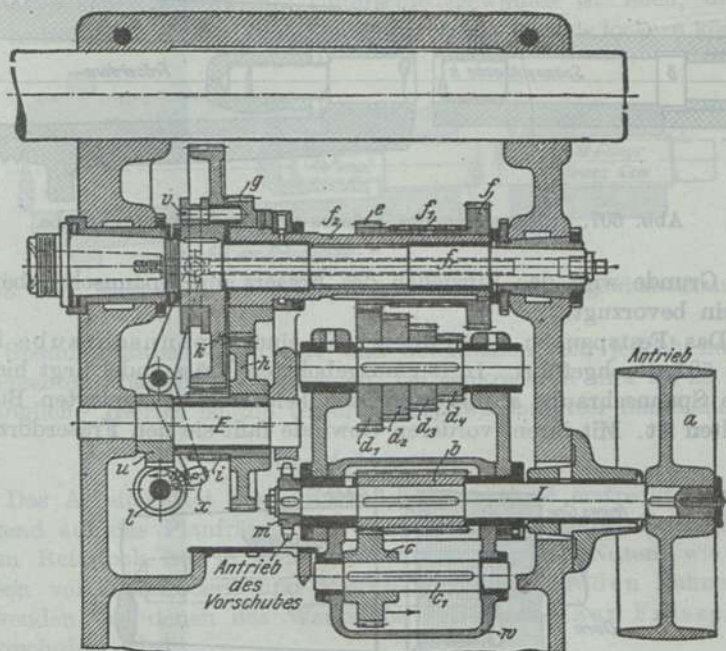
Hauptantrieb der Wanderer-Fräsmaschine.
